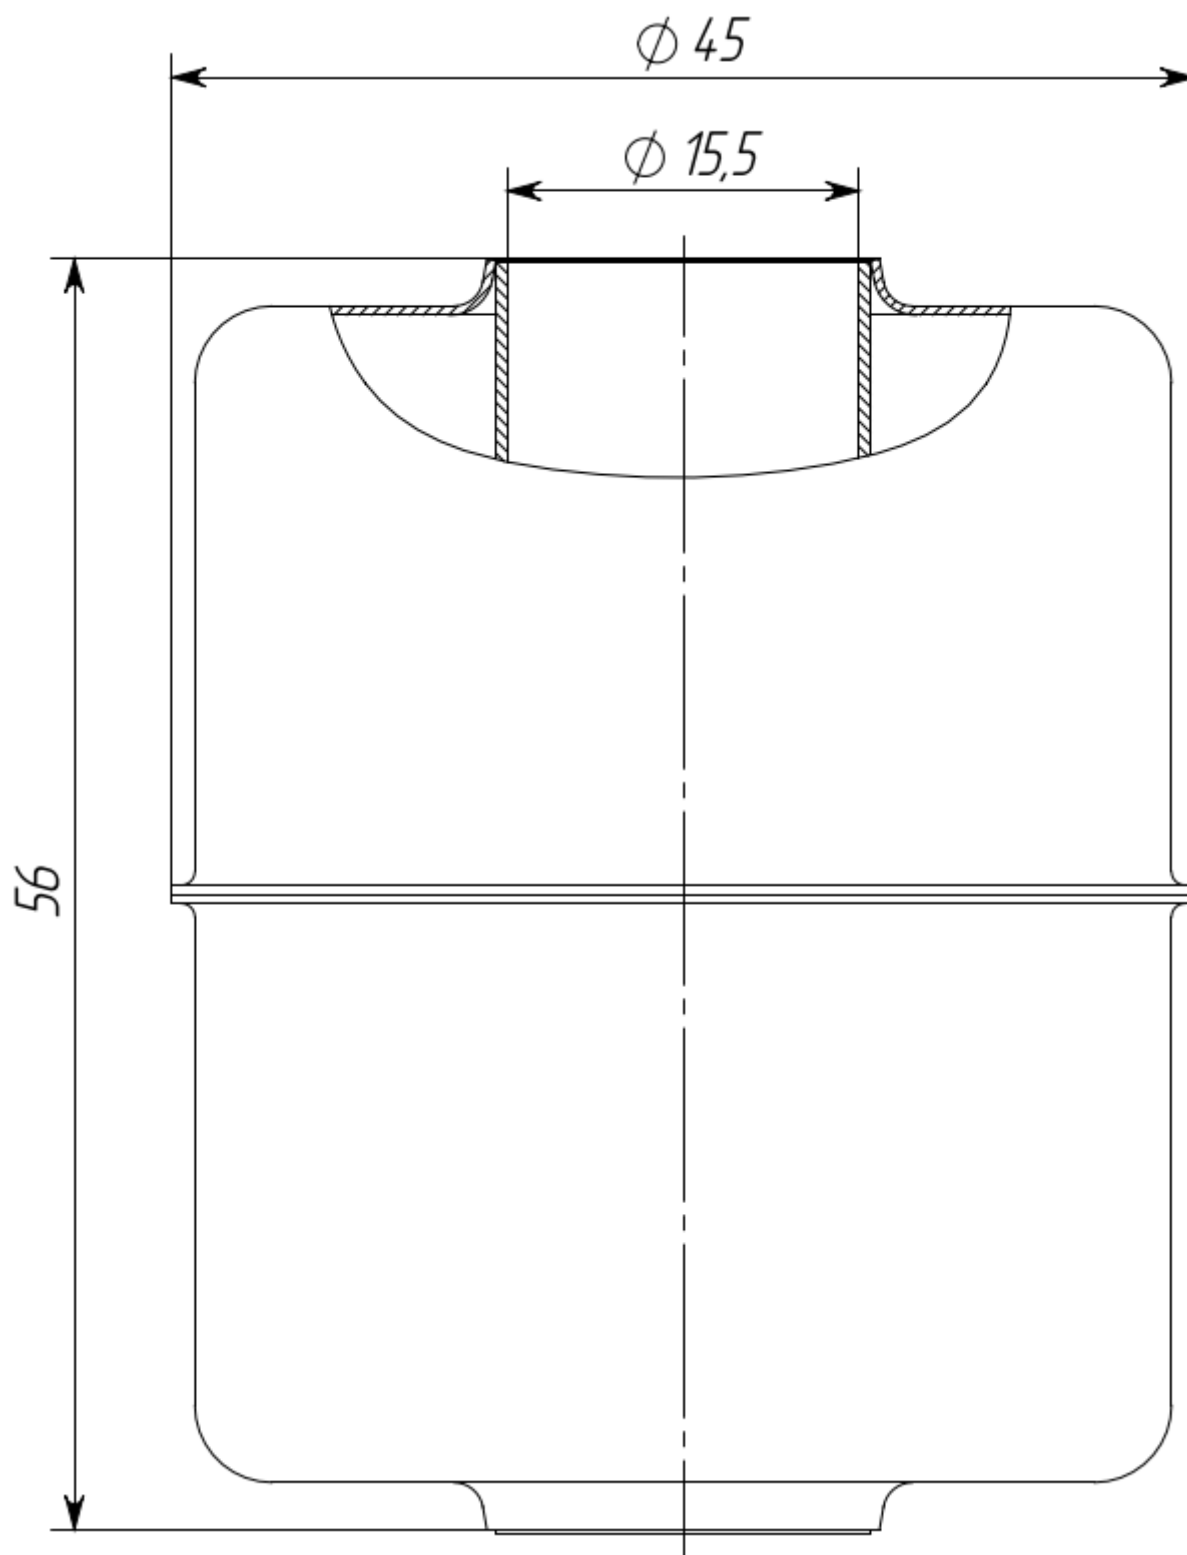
Габаритные и установочные размеры поплавок Н45 (масса 56 г)
